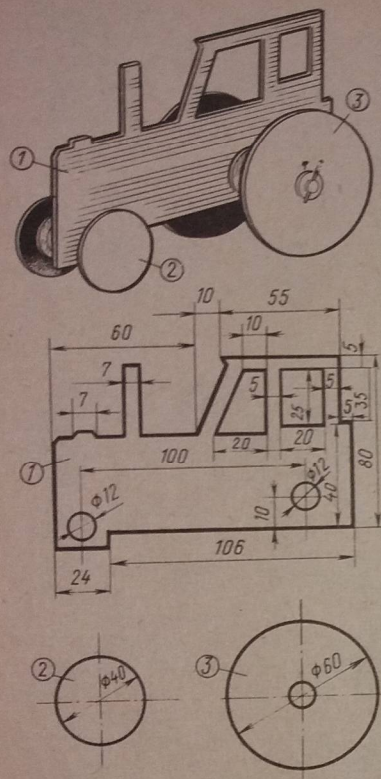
Контурная модель трактора с резиномотором: 1—корпус; 2—переднее колесо; 3—заднее колесо
